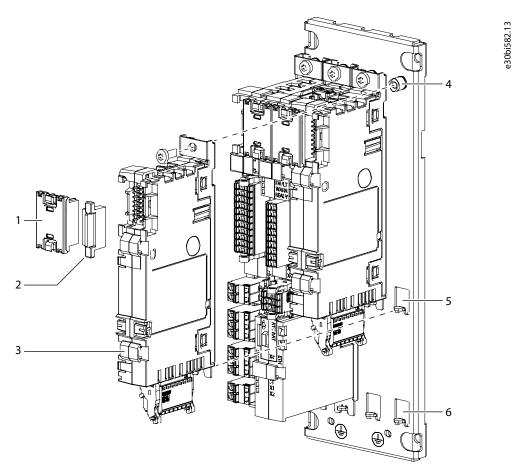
Instalación de una tarjeta en la placa de montaje del compartimento de control
